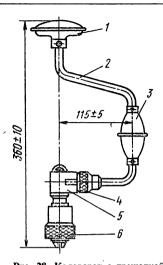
Коловорот с трещоткой: I — головка нажимная; 2 — коленчатый стержень; 3 — ручка; 4 — кольцопереключатель; 5 — храповой механизм; 6 — патрон
